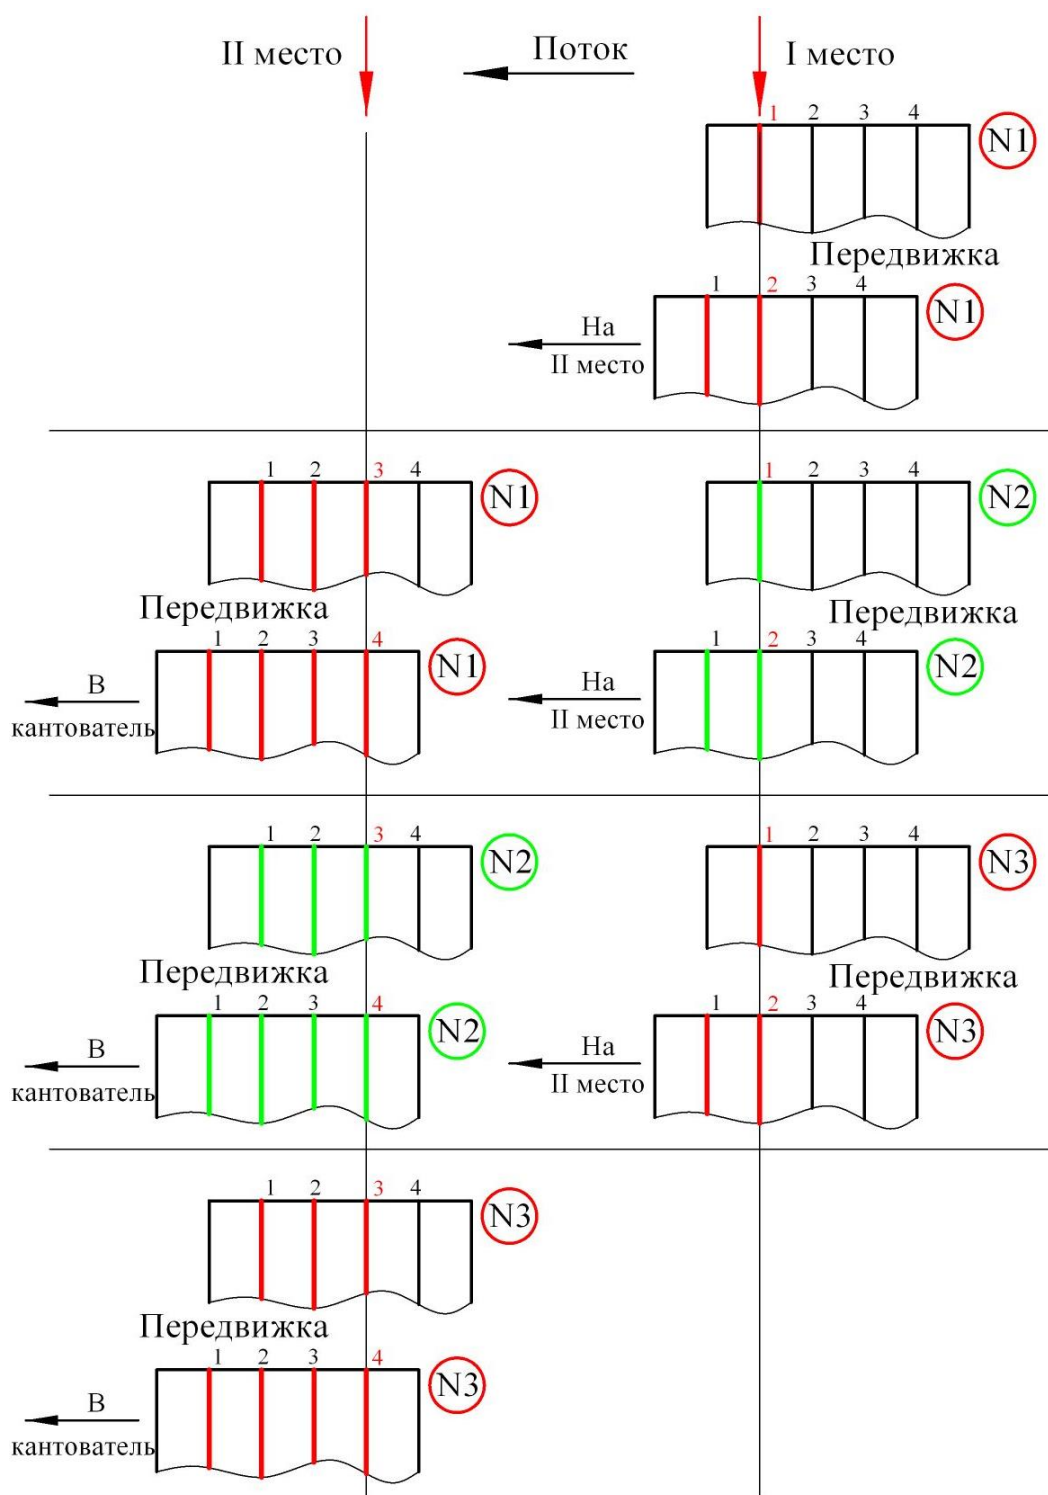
Схема сварки на двухместном стенде четырех стыковых листовых полотнищ:
